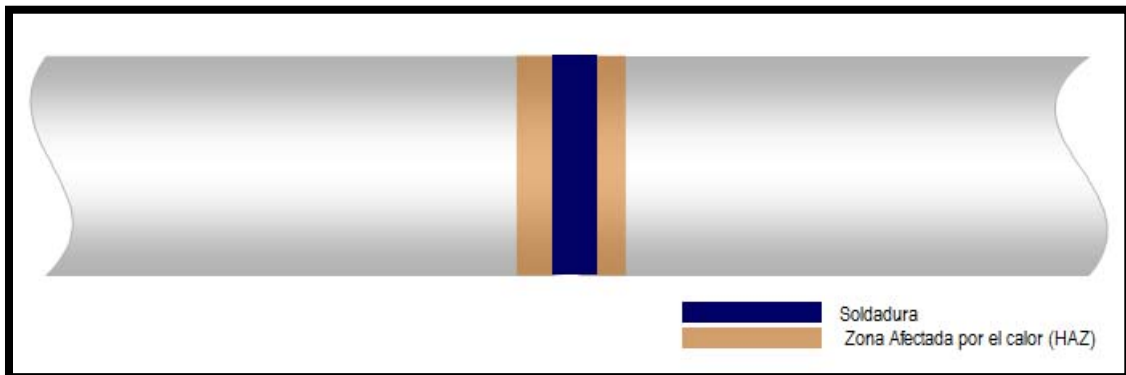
4. Zona de soldadura y HAZ (aproximadamente 3/8" de espesor desde la soldadura).
